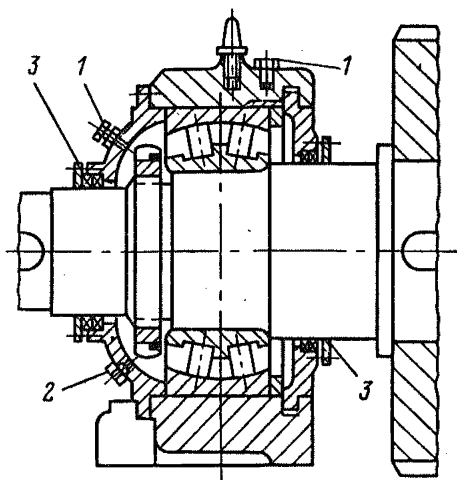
Подшипник приводного вала (смазка жидкая).
